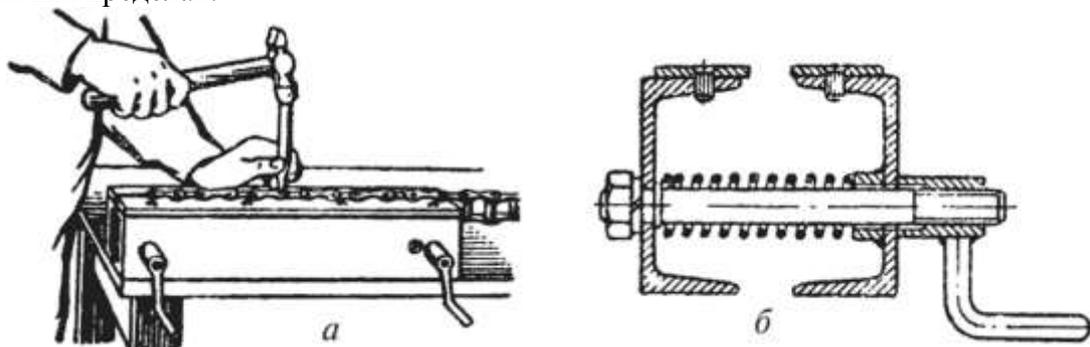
Приспособление для разборки втулочно-роликовых цепей: *a* — общий вид; *б* — вид в разрезе
